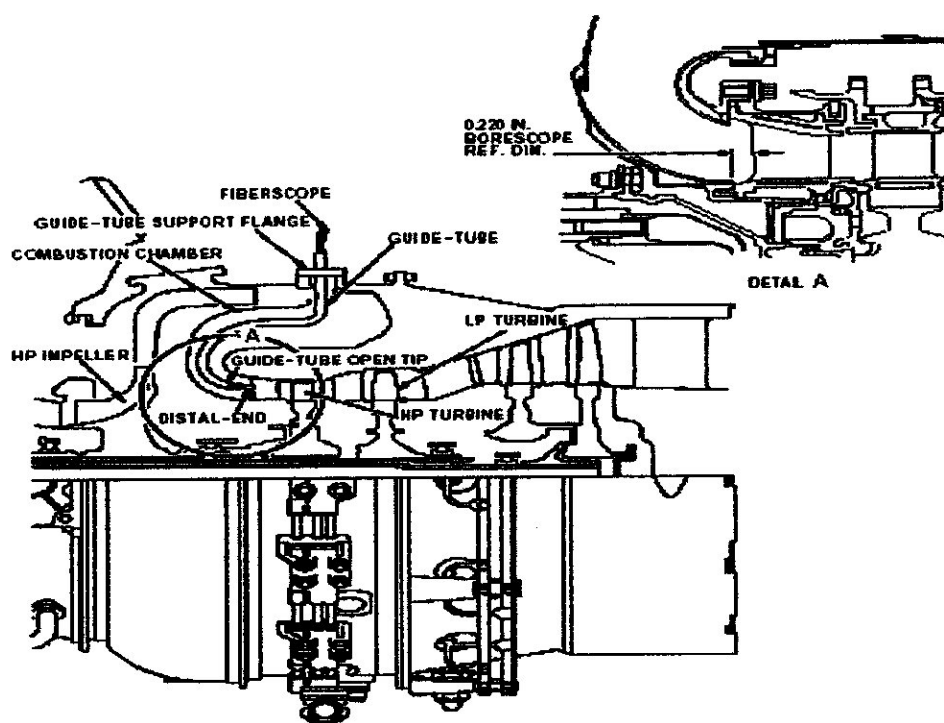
Inspection du stator et des ailettes de la turbine HP.
